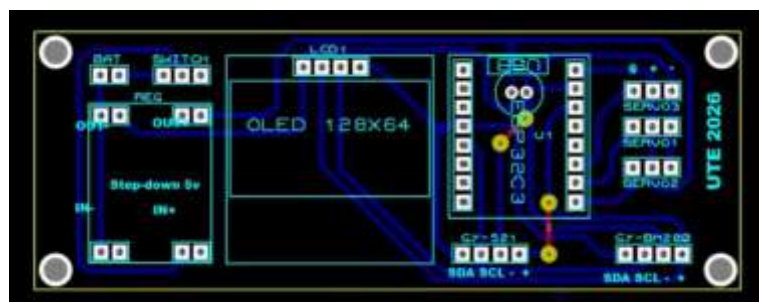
Diseño de pistas y distribución de componentes (Layout) de la PCB del Cohete.
